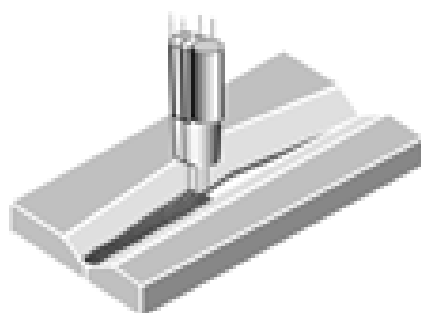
Система отслеживания сварного шва «COMARC»
